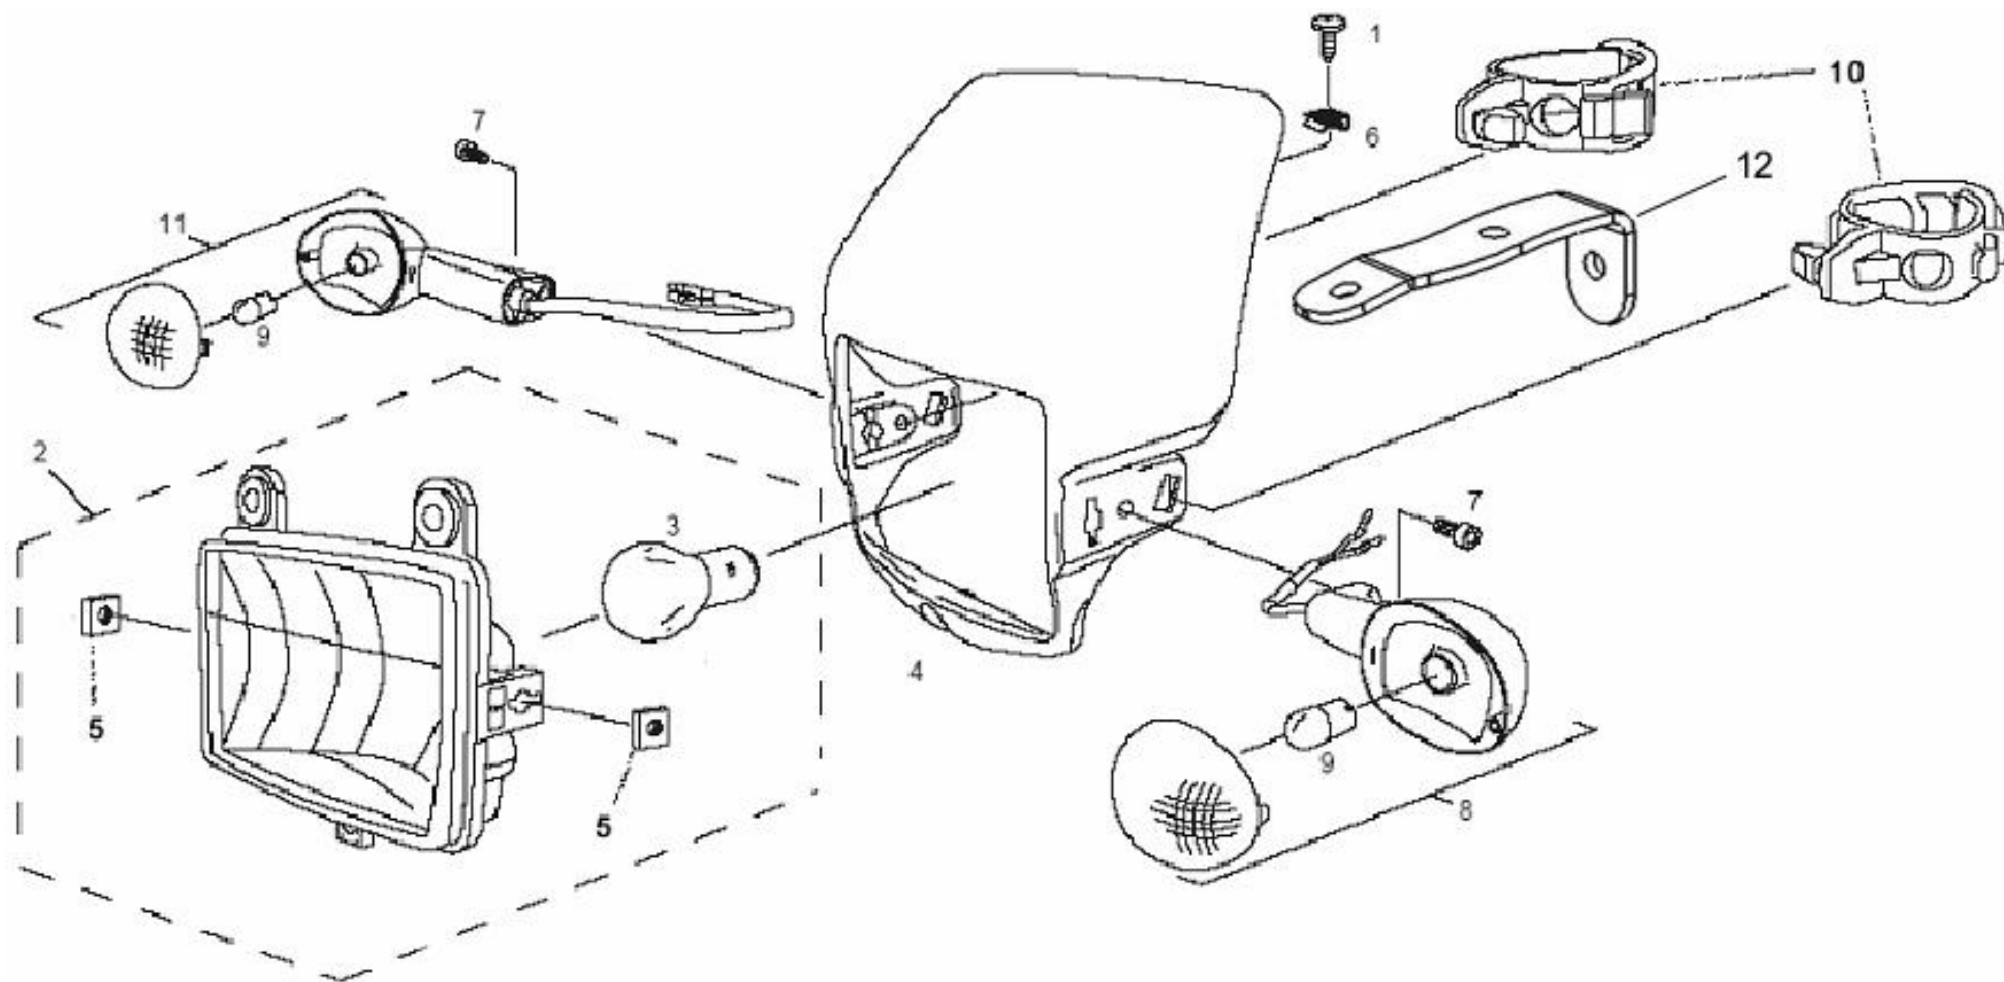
PLAQUE PHARE / HEAD LIGHT / FARO DELANTER
